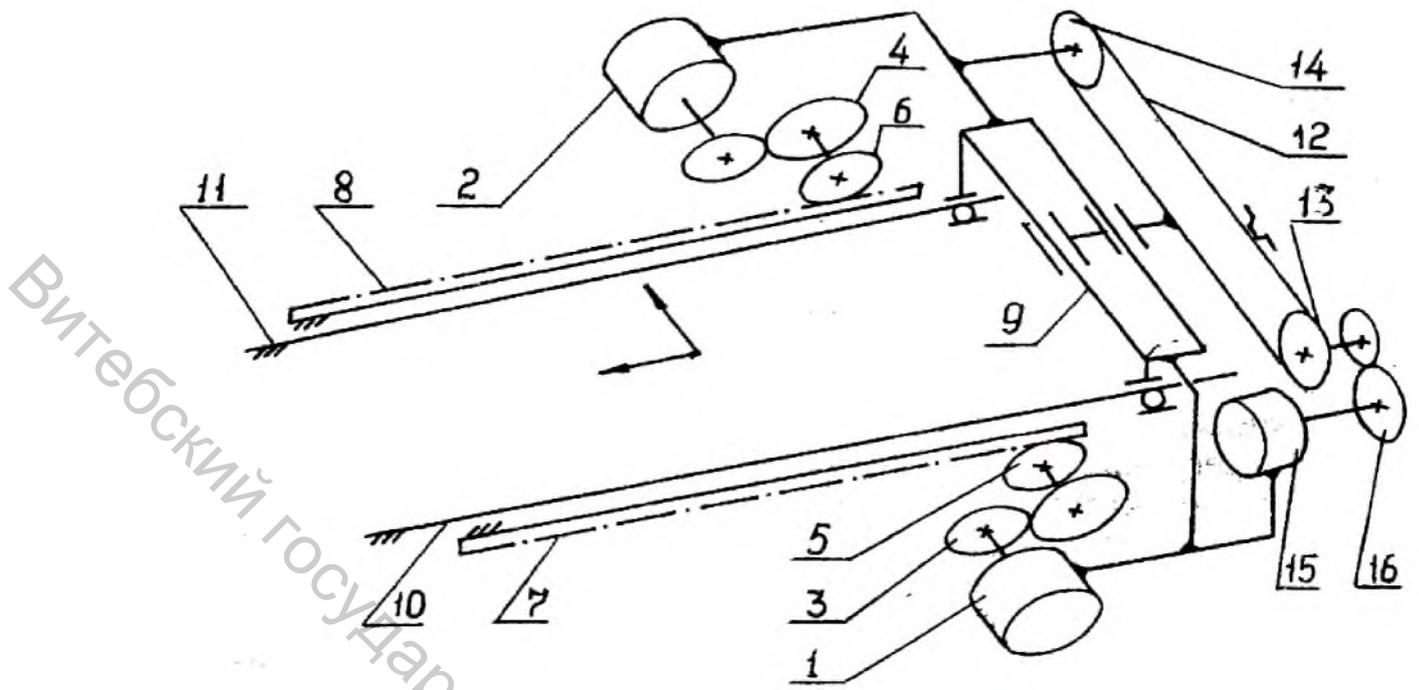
Механизм перемещения раскройной головки (портал)
